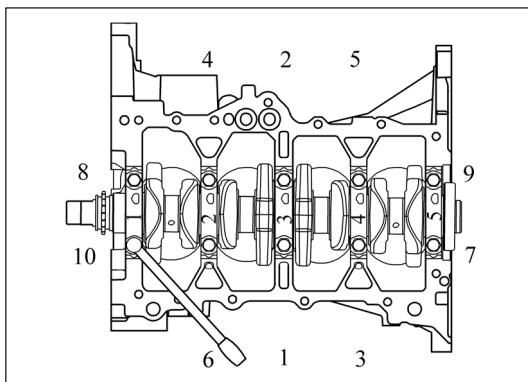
Установка крышек коренных подшипников и нижних вкладышей коренных подшипников
